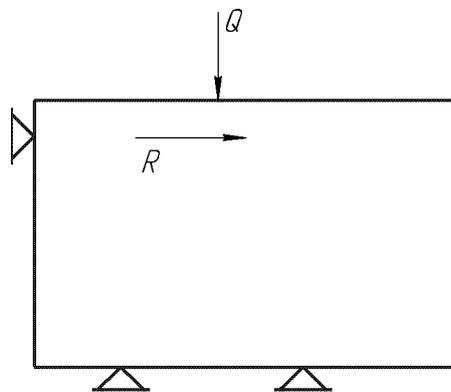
Схема дії сил на заготовку деталі «Вал-шестерня Д02210.5»
